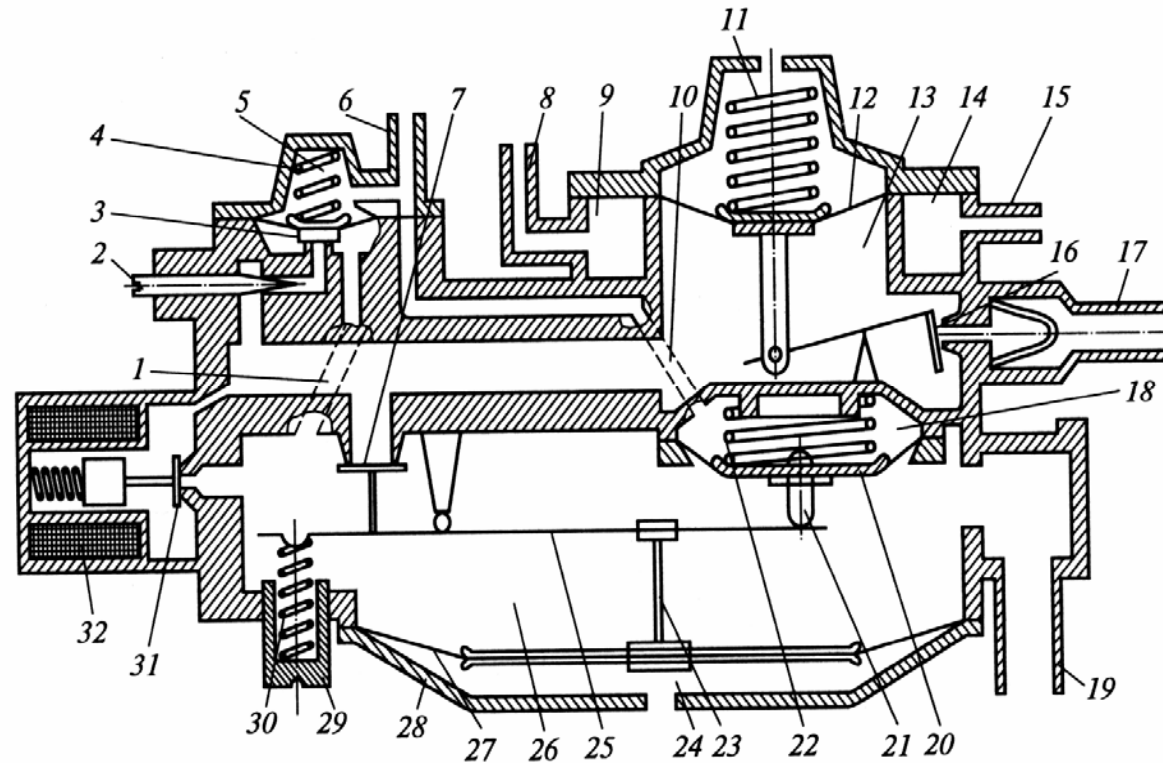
Схема редуктора-испарителя низкого давления НЗГА:
